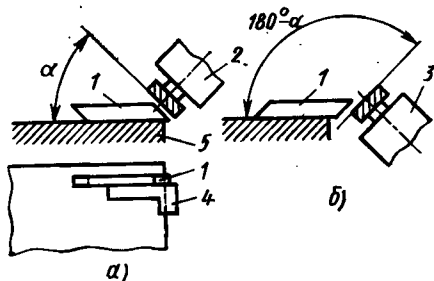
Схема настройки фрезерных суппортов для обработки косых плоскостей разреза диафрагмы
